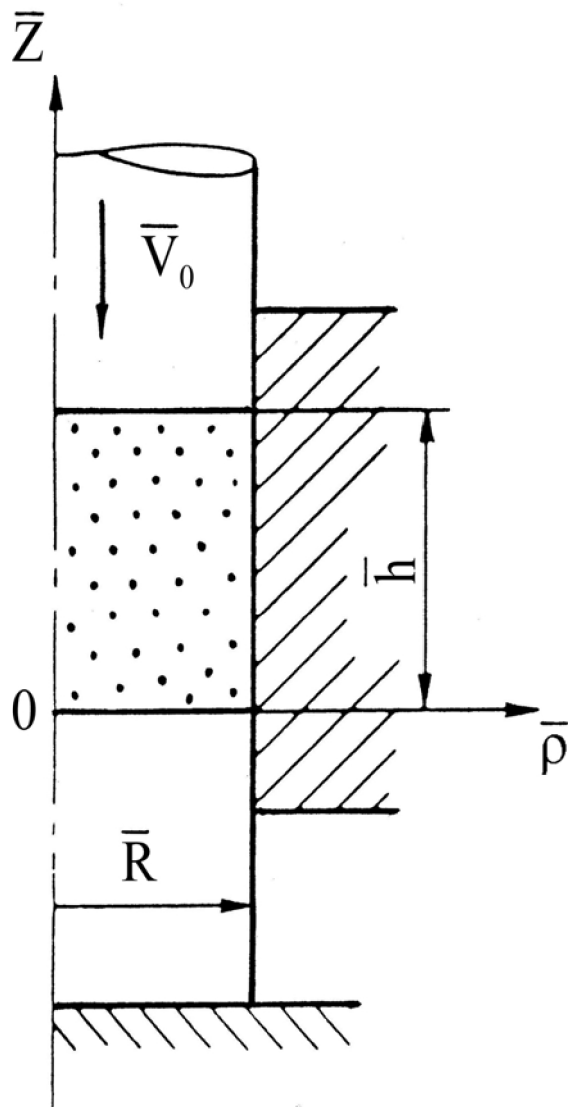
Схема формирования порошковой заготовки в закрытой матрице
